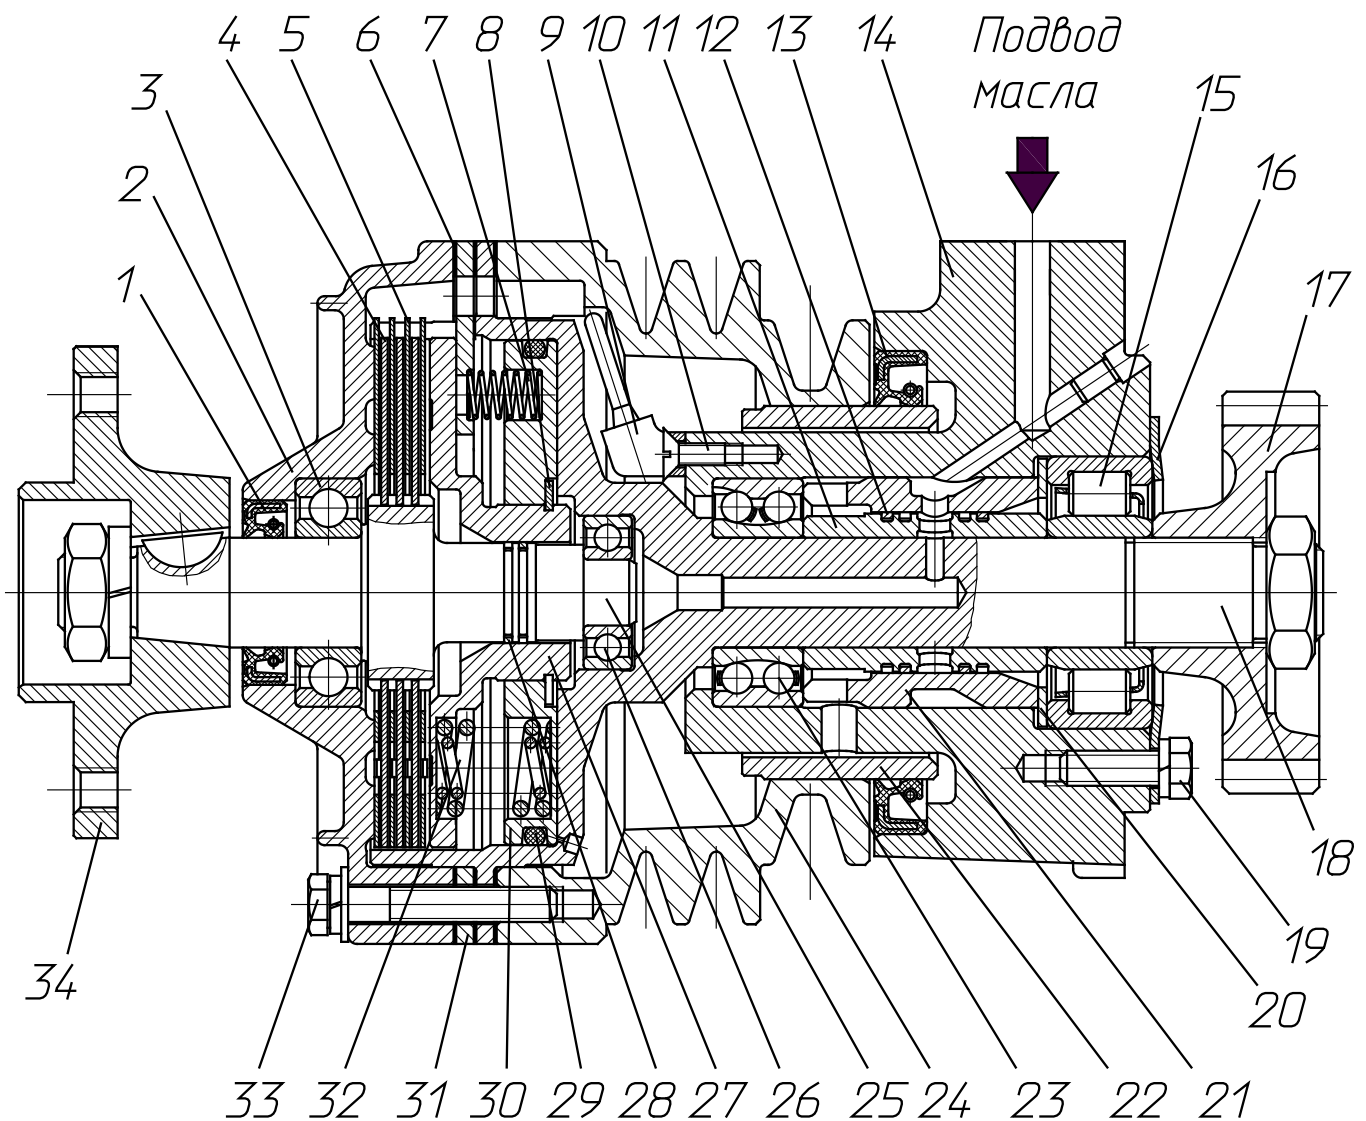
Привод вентилятора 7511.1308011-30
